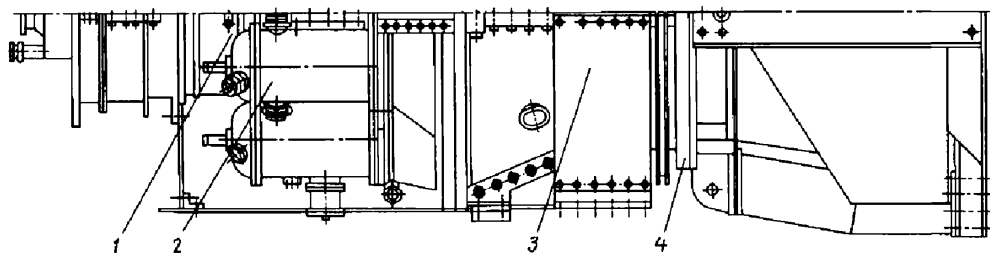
Двухвальный газотурбинный двигатель:
